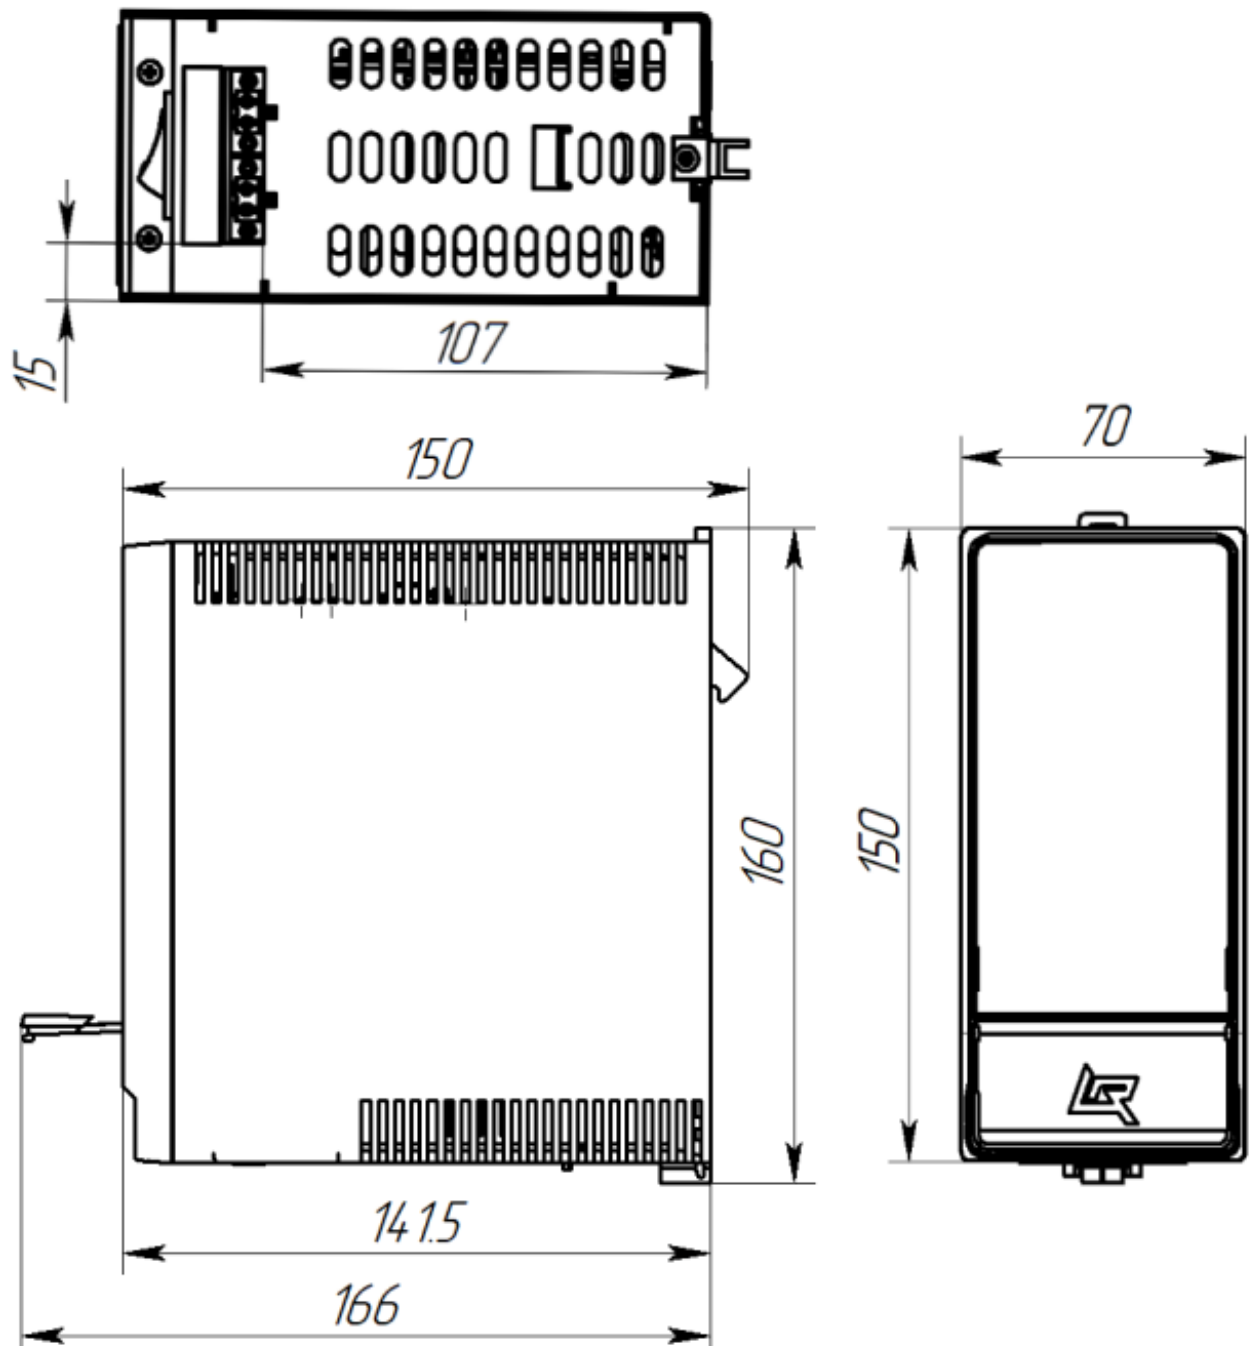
Габаритные и присоединительные размеры модуля питания в пластмассовом корпусе
